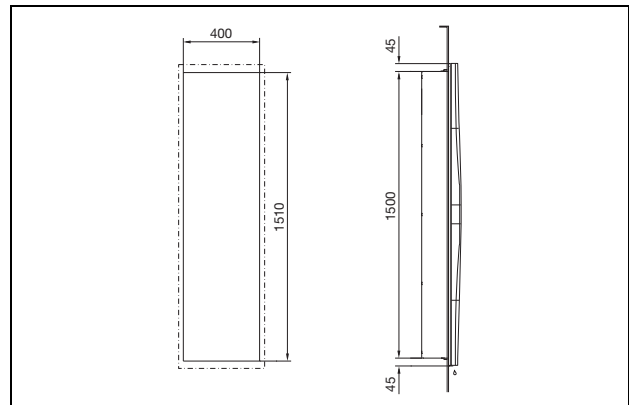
3303.xxx, 3361.xxx – montaż całkowicie wewnętrzny
